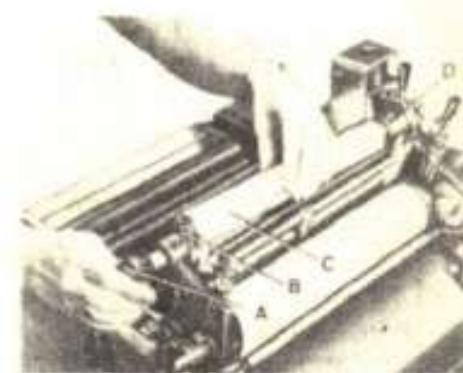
Instalación del Rodillo de la Fuente de Repelex
